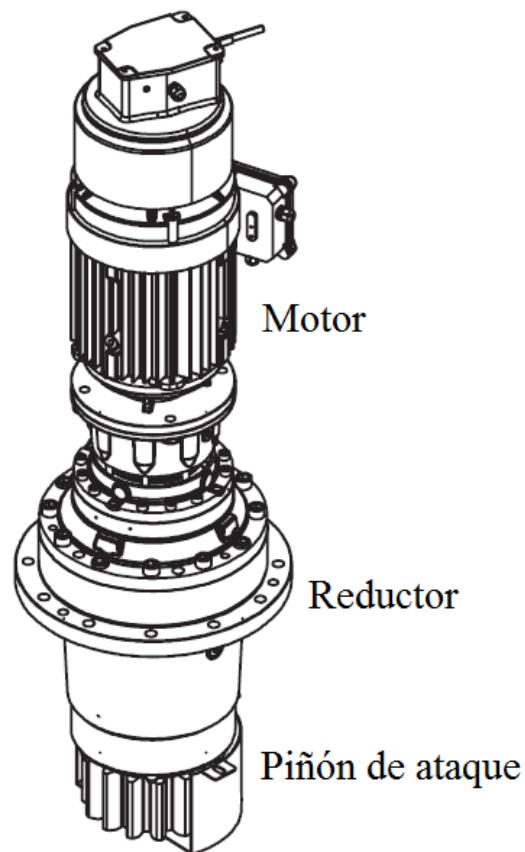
Mecanismo de giro con sus partes que lo componen
